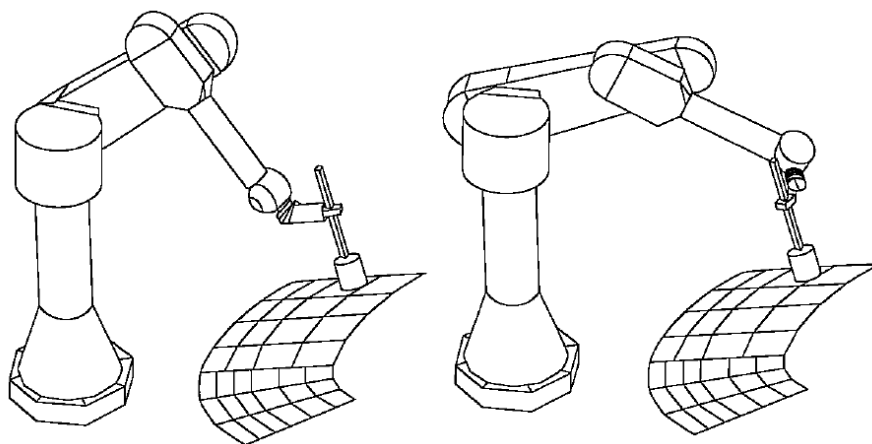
Manipulador com 6 GDL com ferramenta simétrica [Adaptado de Craig, 2012].
